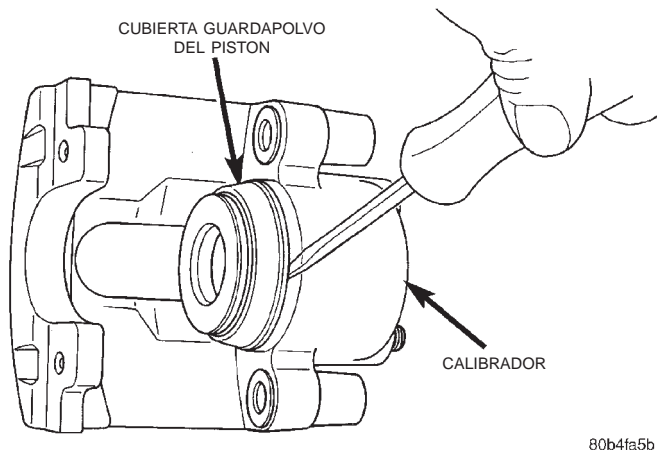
Desmontaje de la cubierta guardapolvo del pistón del calibrador
